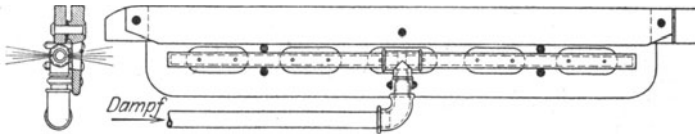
Mittelstab eines Planrostes mit Dampfbrause. Ausführung der Eßlinger Maschinenfabrik.
